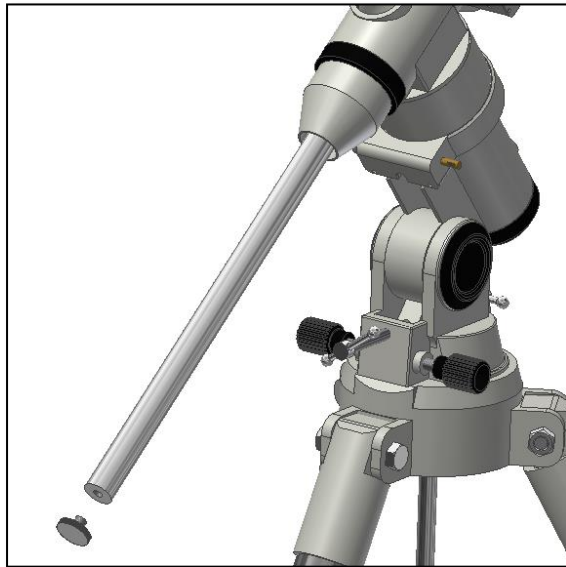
Sicherungsschraube herausschrauben, um das Gegengewicht aufschieben zu können
